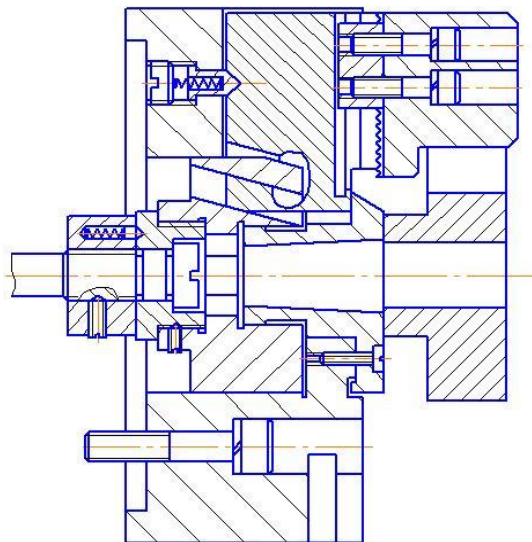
Схема закріплення заготовки в трьохкулачковому патроні.
